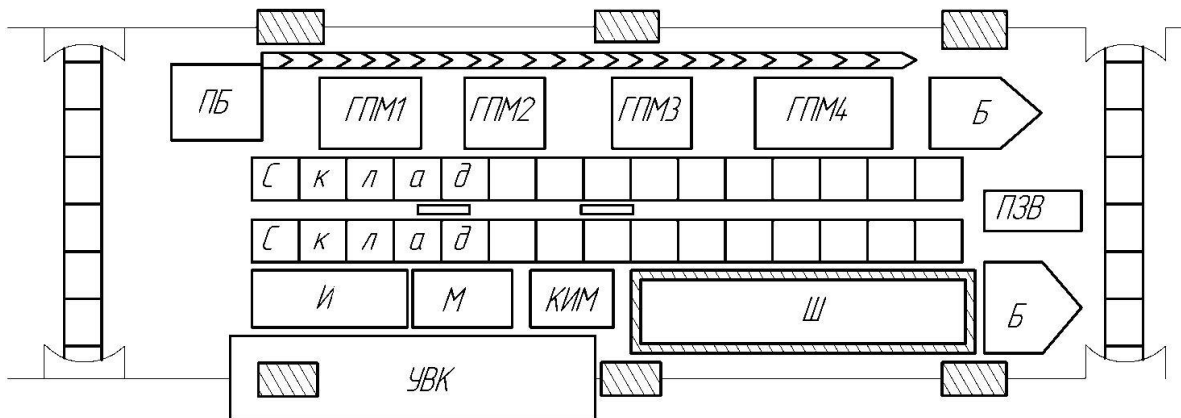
План ГАД с легкими токарными ОЦ
